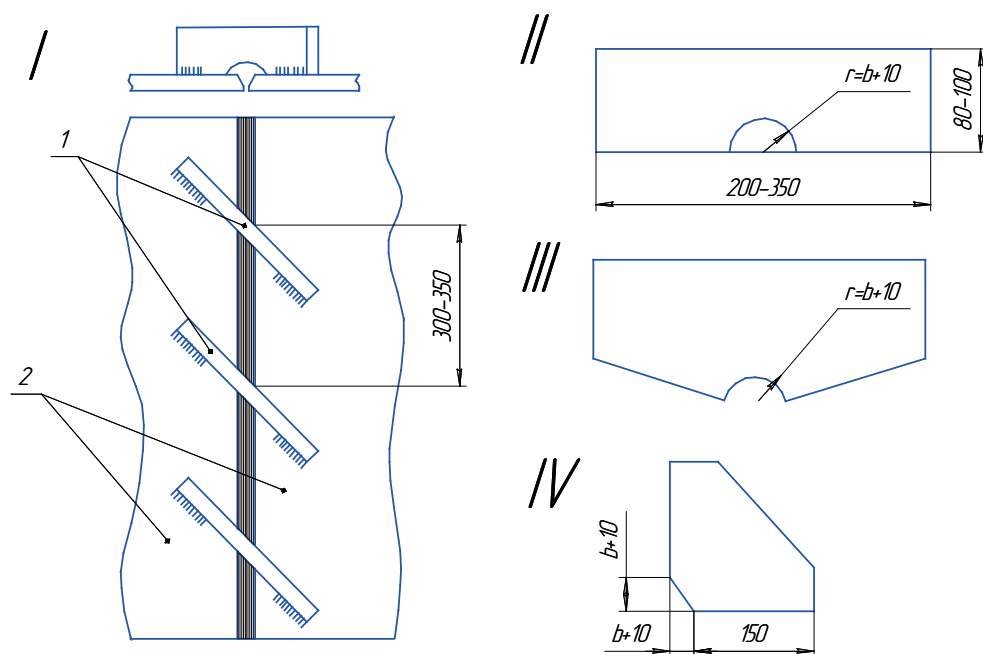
Эластичное крепление деталей при сварке с помощью гребенок:
